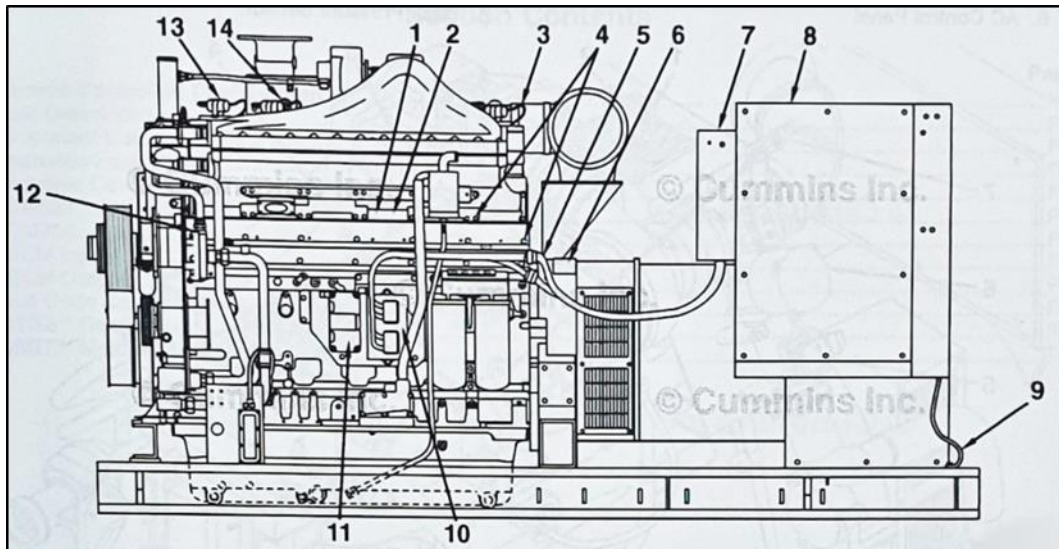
Les composants électronique, vue latérale gauche [46]
